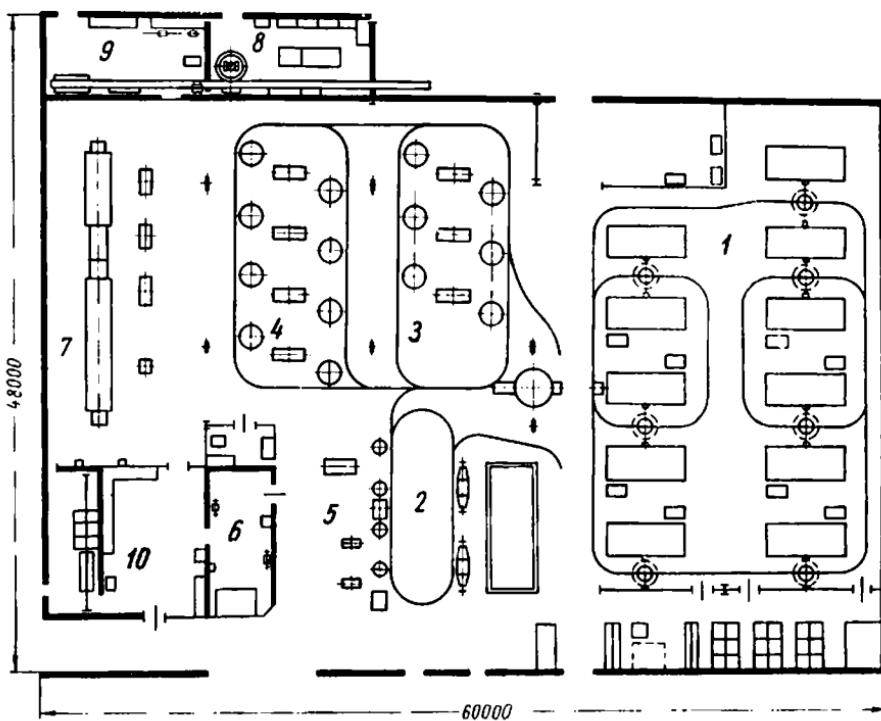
План цеха литья в металлические формы из алюминиевых и медных сплавов
